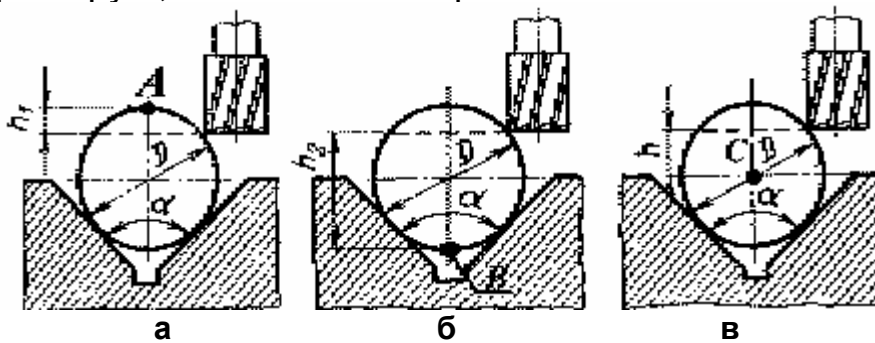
Вимірювальні бази при обробленні вала в призмі
